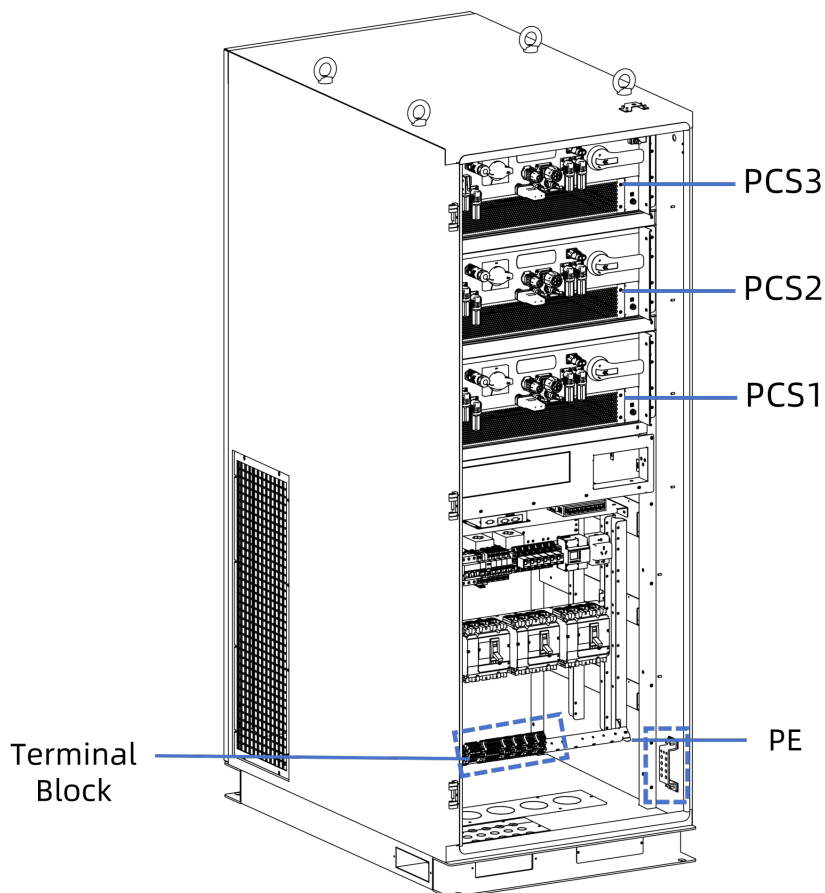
Positionen der Komponenten – AC-Steuergehäuse
